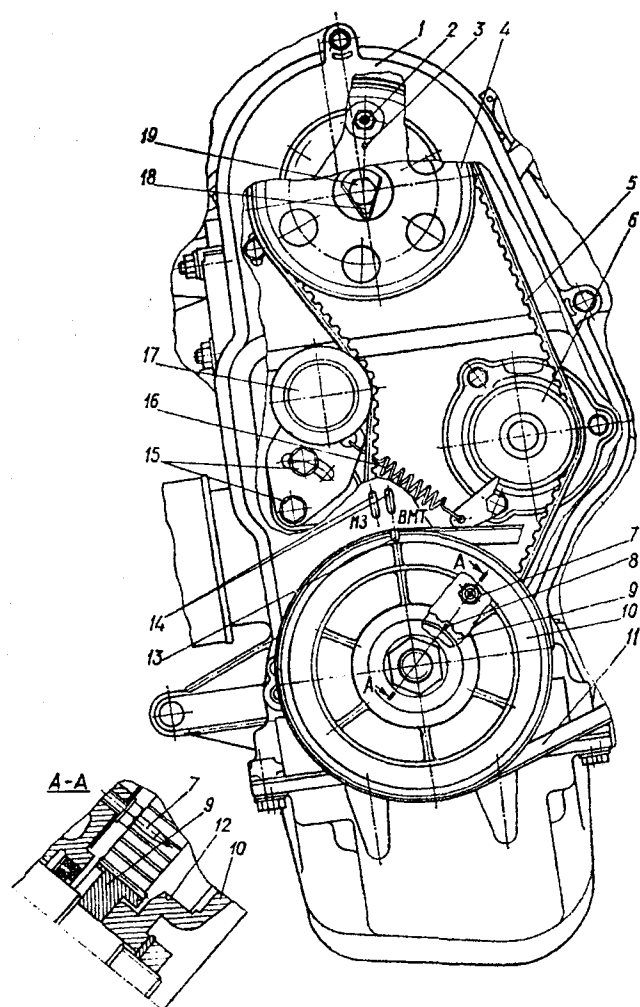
Привод распределительного вала: 1 – наружный кожух плосkozубчатого ремня; 2 – стрелка установки ведомого шкива распределительного вала; 3 – метка на шкиве распределительного вала; 4 – ведомый шкив распределительного вала; 5 – плосkozубчатый ремень; 6 – шкив водяного насоса; 7 – стрелка установки ведущего шкива привода распределительного вала в ВМТ; 8 – метка ВМТ на ведущем шкиве; 9 – ведущий шкив привода распределительного вала; 10 – шкив привода генератора; 11 – ремень привода генератора; 12 – метка ВМТ (сверленное гнездо диаметром 4 мм) на ступице шкива привода генератора; 13 – метка ВМТ на шкиве привода генератора (прорез на наружной стороне шкива); 14 – метки ВМТ и МЗ на верхнем кожухе зубчатого ремня; 15 – болты кронштейна натяжного ролика; 16 – пружина натяжного ролика; 17 – натяжной ролик; 18 – отгибная шайба; 19 – болт крепления шкива
